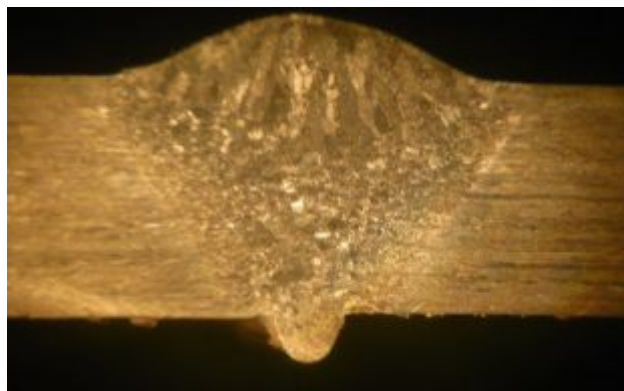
Микрошлиф сварного шва приварки фланца. Материал VT6C (×5)
